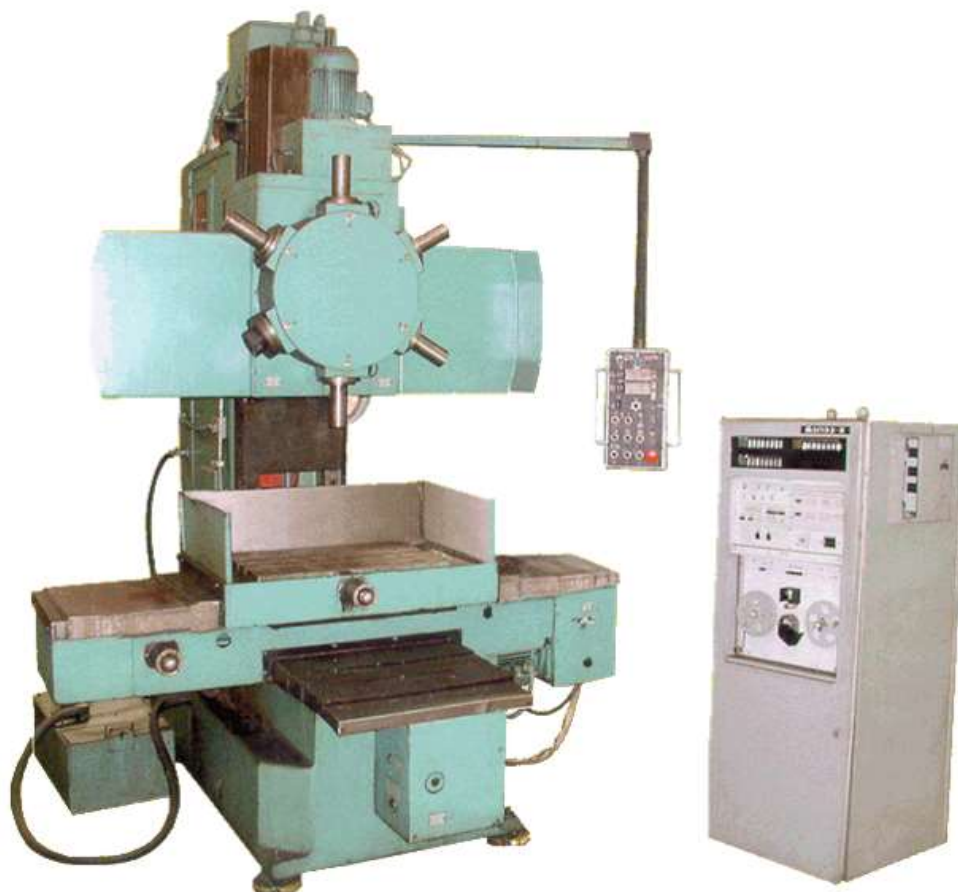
Вертикально-свердильний верстат мод.2P135Ф2
